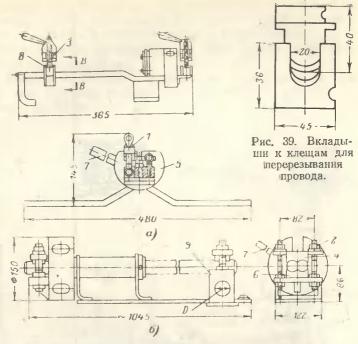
Станок для скручивания овальных соединителей. а—по черт. МИ-189; б—по черт. МИ-190; 1—откидной болт; 2—гайка; 3, 4—верхние плашки; 5, 6—нижине плашки; 7—вороток; 8—ползушка; 9—стойка.
